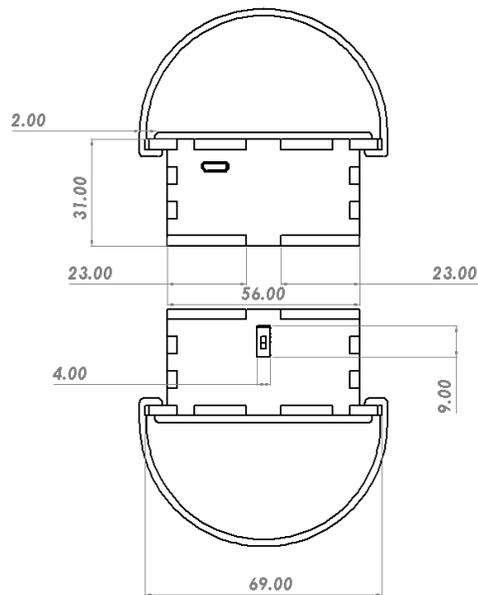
Planos frontal y posterior del dispositivo vibrador final.
